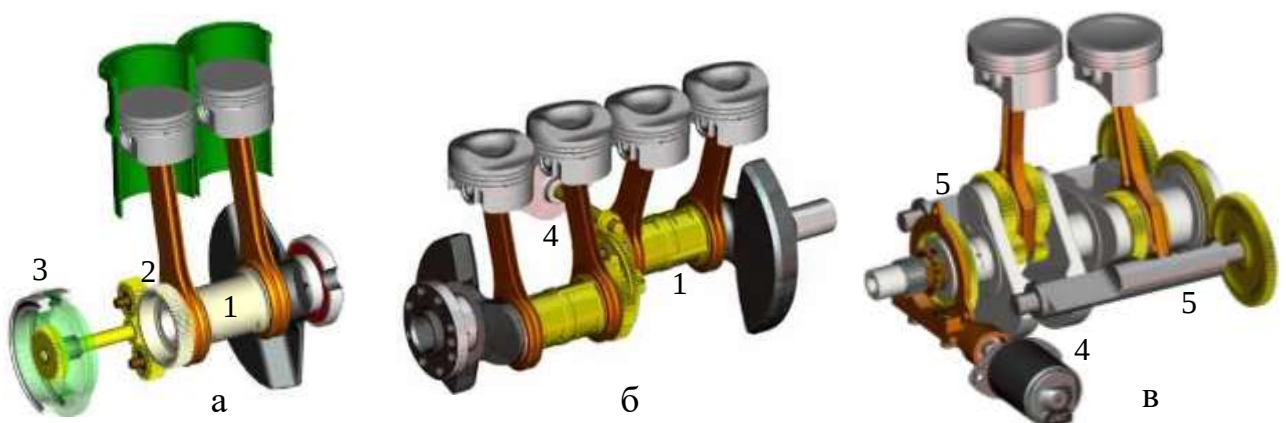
Конструкції двигуна VCR Go Engine з ексцентриковими валами:
